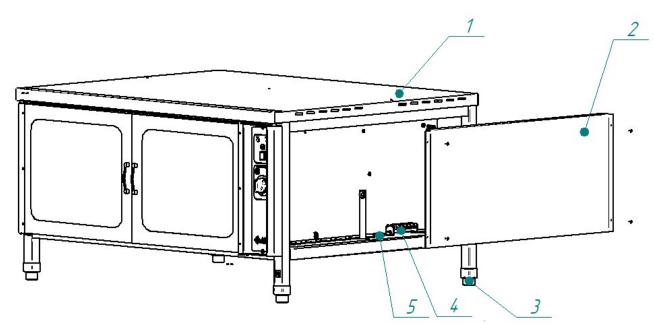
Схема сборки шкафа ШРТ 4-ЭШ-01
